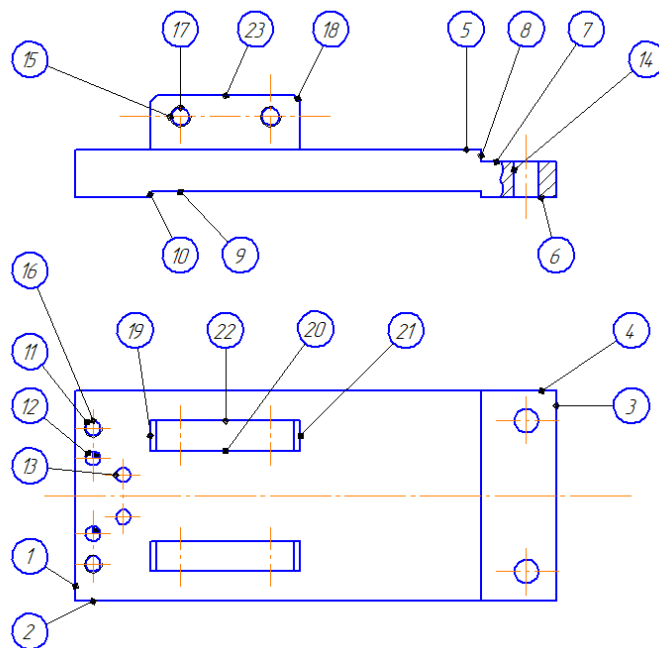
Нумерація поверхонь деталі “Основа”
